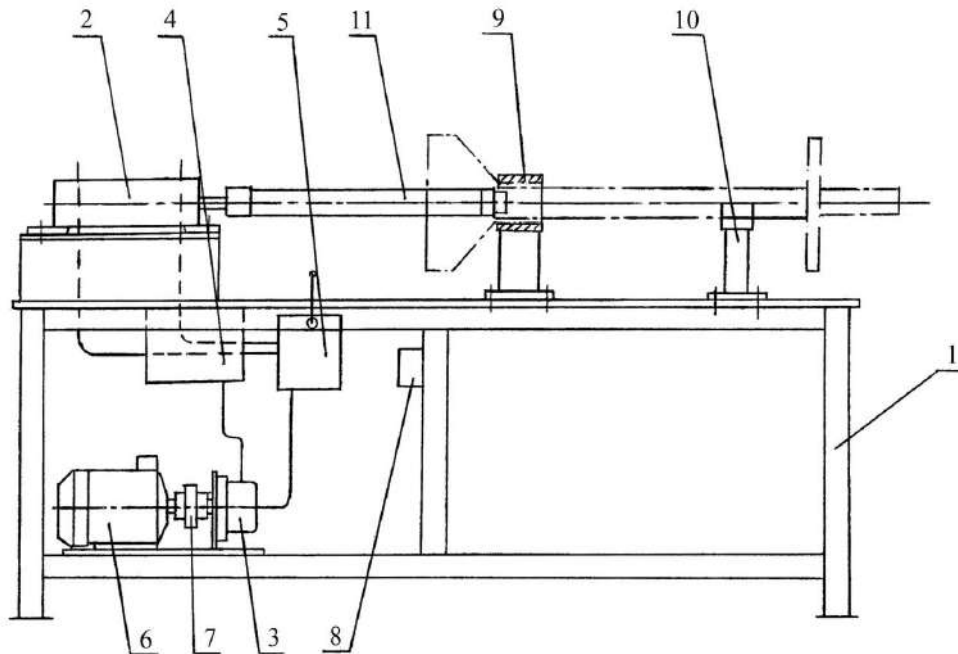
Схема пресса для перепрессовки кожухов полуосей.
